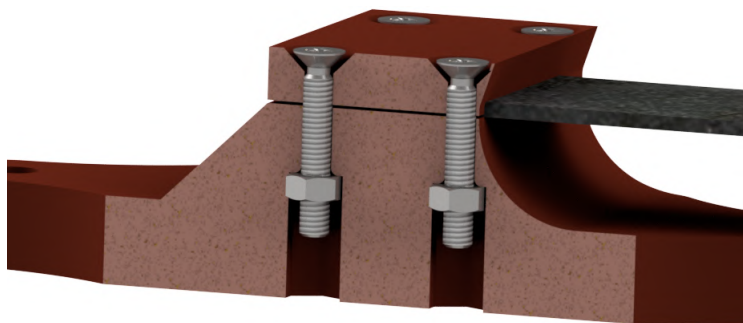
Uloženie magnetického obvodu a s cievkou
